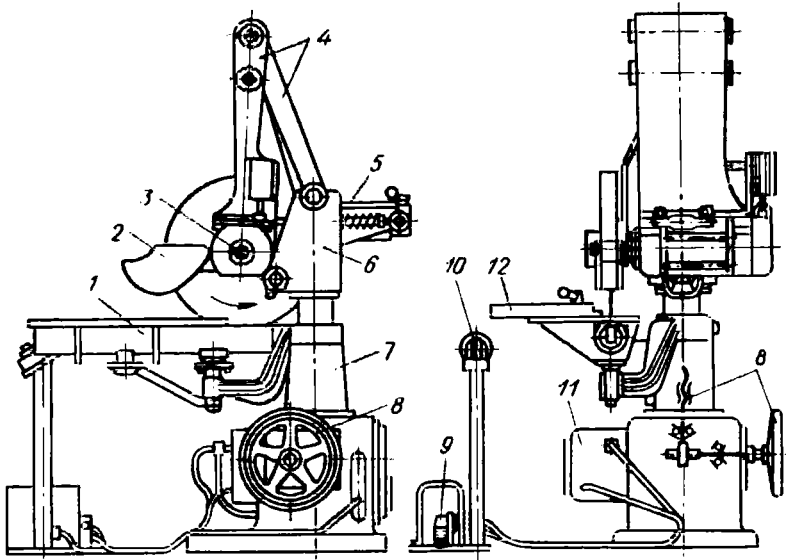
Схема торцовочного станка ЦМЭ-3А:
